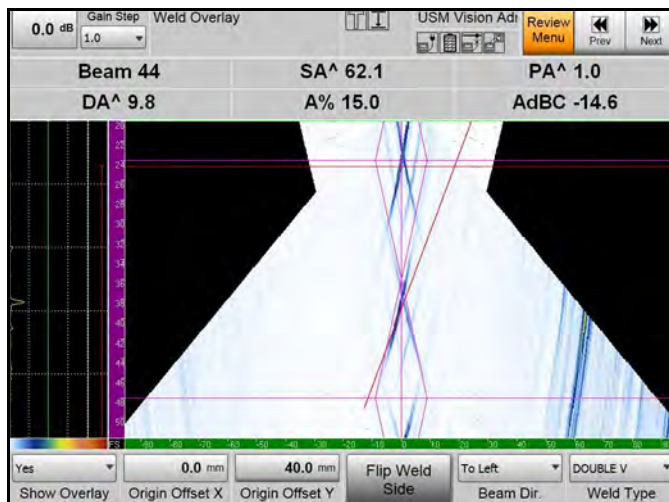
Направленный слой сварного шва с кнопкой переворачивания (Flip)
